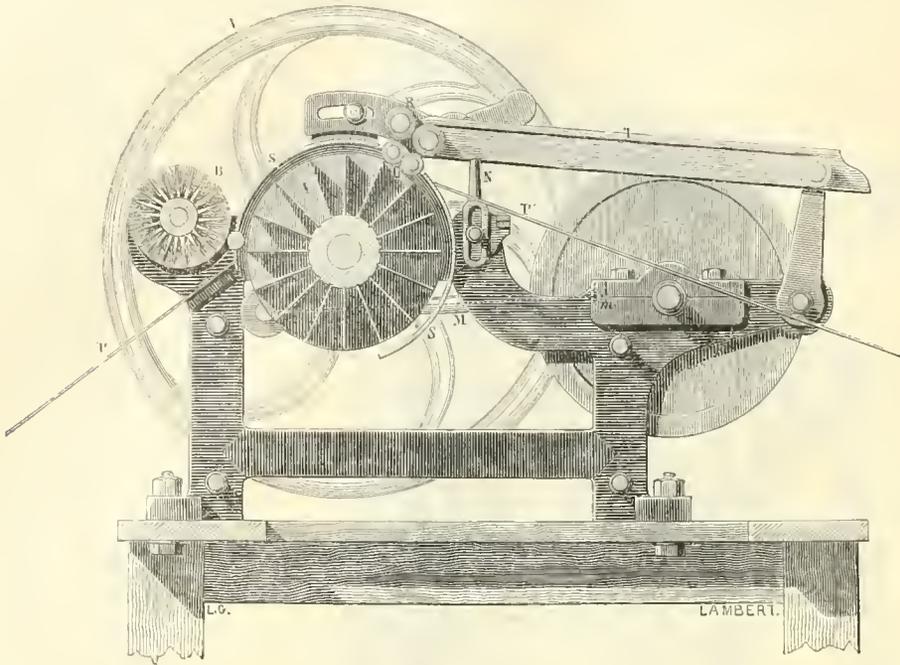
Coupe de la première machine à égrener le coton, de François Durand.
